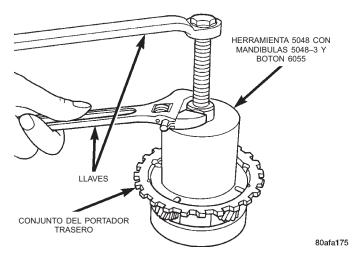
Desmontaje del cono de cojinete del portador trasero
